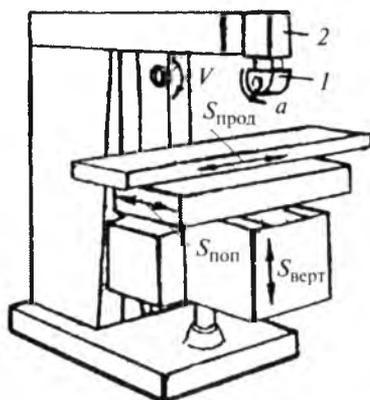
Широкоуниверсальный фрезерный станок:
